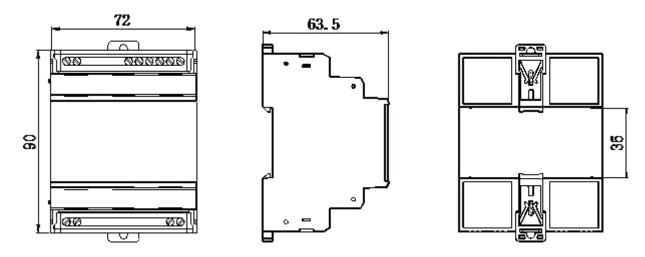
Внешний вид и габаритные размеры модуля измерительного КСМ-М2
